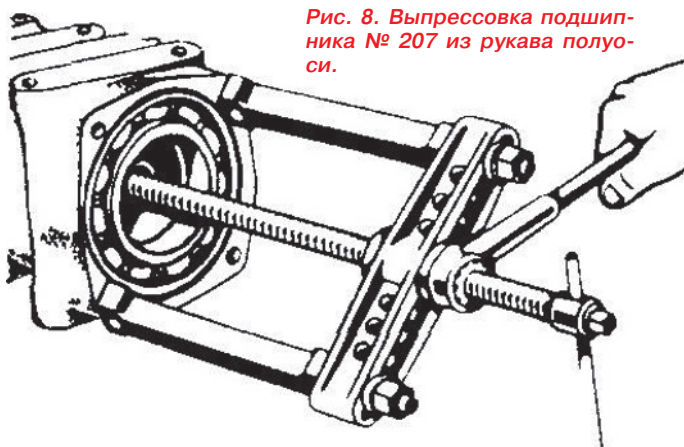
Выпрессовка подшипника № 207 из рукава полуоси.
